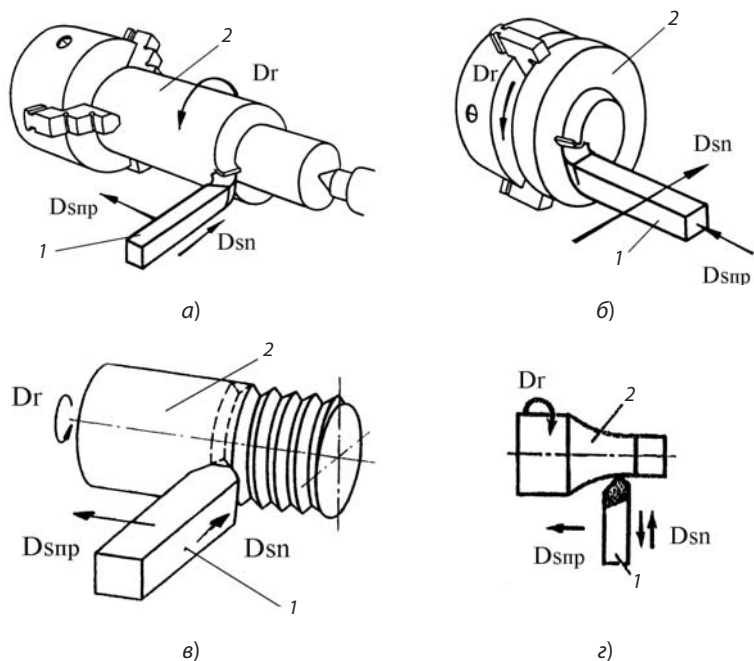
Схемы формообразования поверхностей резанием на токарных станках:
